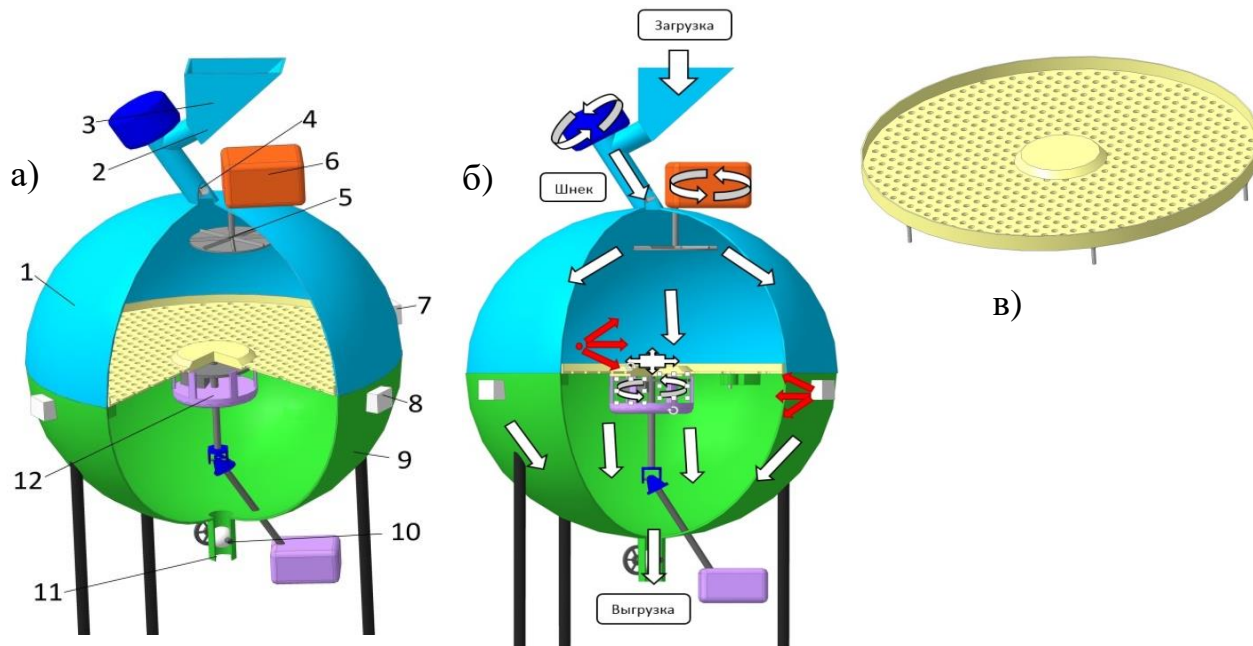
СВЧ-размораживатель непрерывно-поточного действия с полусферическими резонаторами: а) – общий вид; б) – технологическая схема; в) неферромагнитное основание; 1 – верхний полусферический резонатор; 2 – измельчитель с загрузочной емкостью 3 и шнеком 4; 5 – диэлектрический диск; 6 – перфорированное неферромагнитное основание; 7 – магнетроны с волноводами на верхнем резонаторе; 8 – магнетроны с волноводами на нижнем резонаторе; 9 – нижний полусферический резонатор; 10 – шаровой кран; 11 – заградительный волновод; 12 – вибратор диэлектрический
